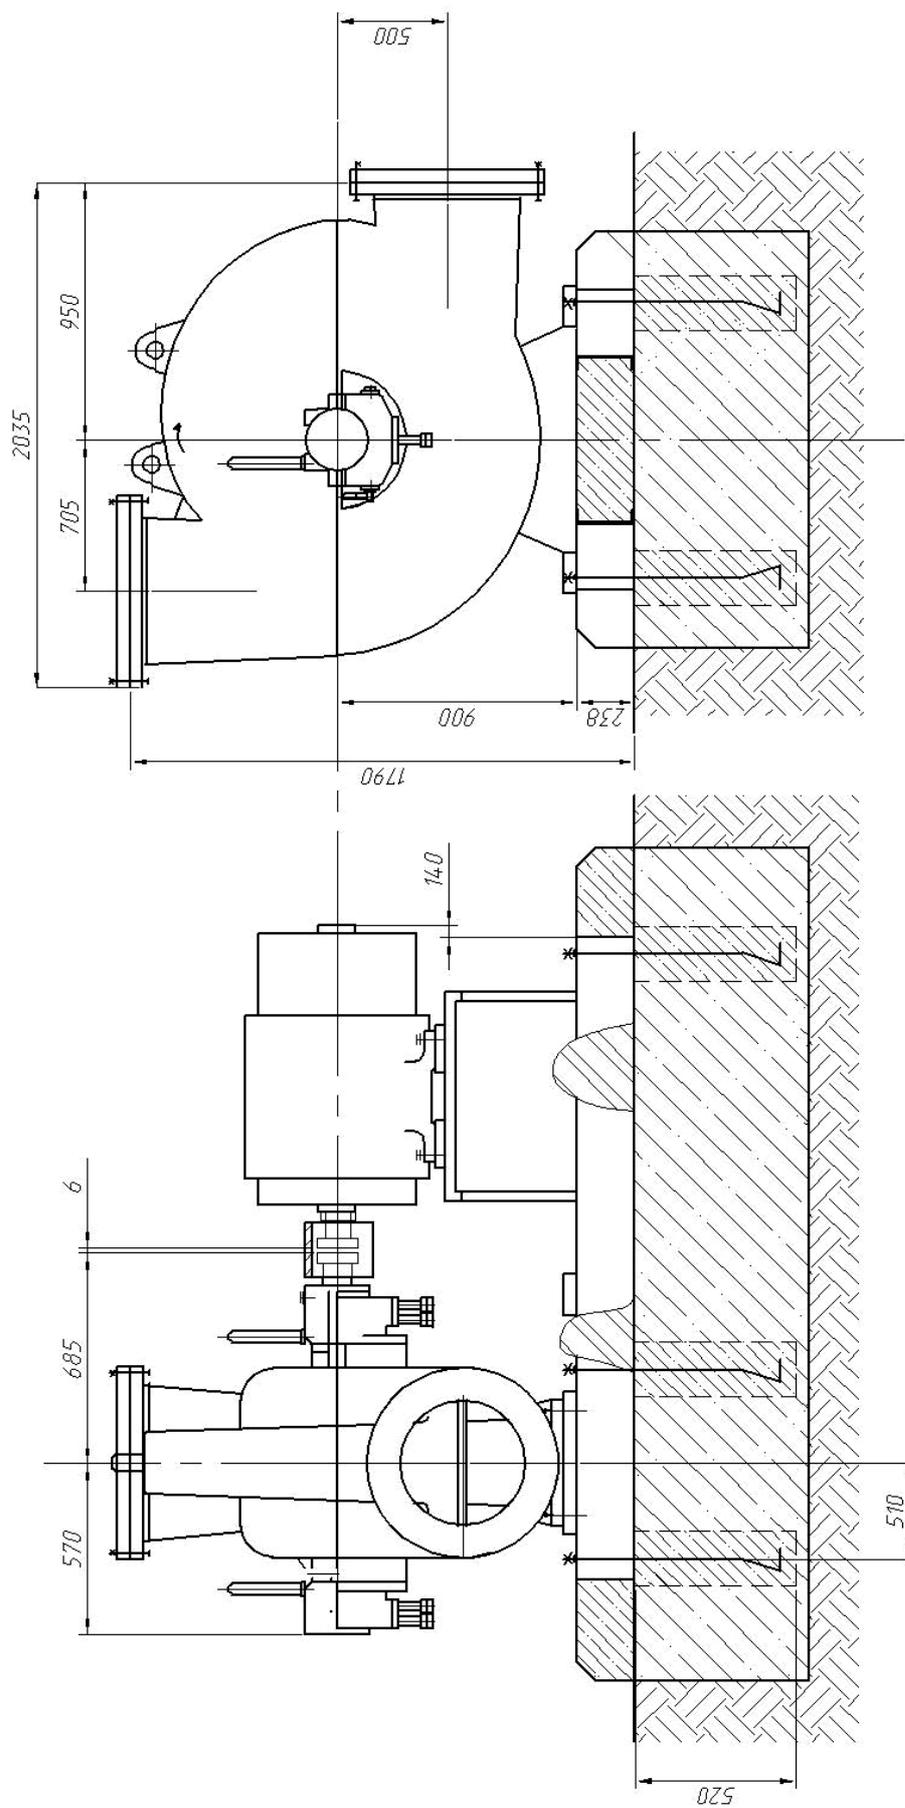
Габаритные размеры газодувки 2ТГ-300-1,18, воздуходувки 2ТВ-300-1,18
